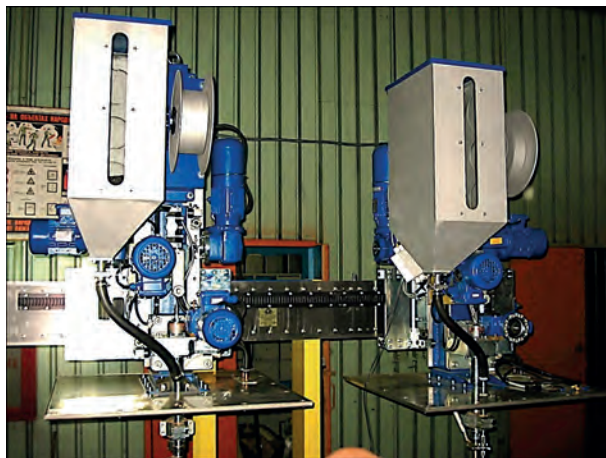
Загальний вигляд здвоєних зварювальних автоматів А1569М для автоматичного зварювання під флюсом у вузький зазор циліндричних виробів
